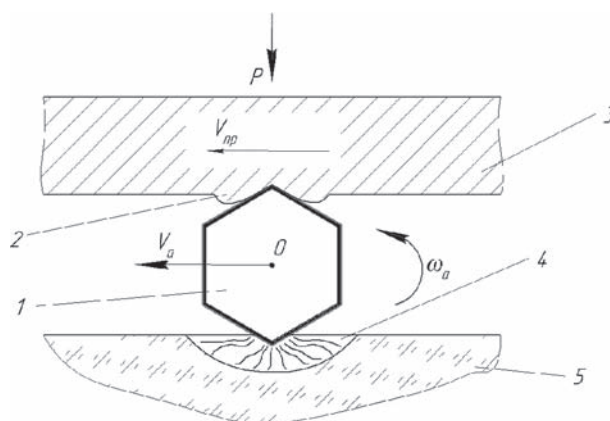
Схема контактного взаимодействия перекатывающегося абразивного зерна с поверхностью инструмента и обрабатываемой заготовки
